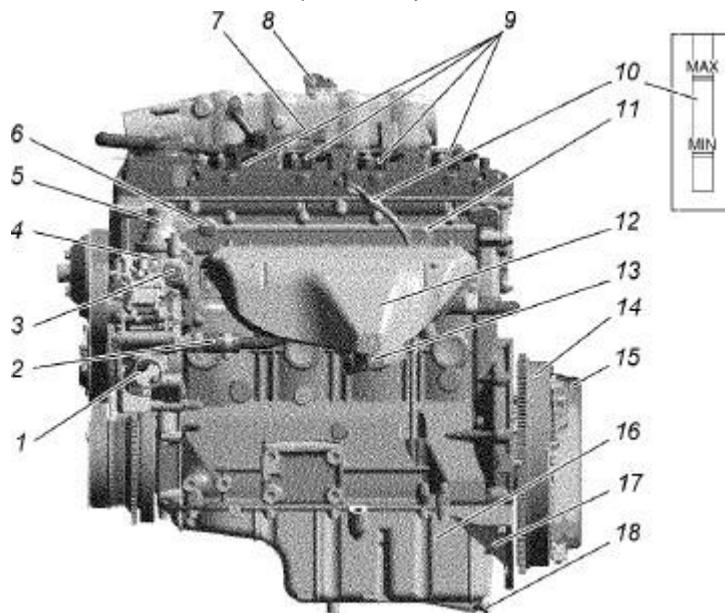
Motor ZMZ-409051 (vista izquierda):
